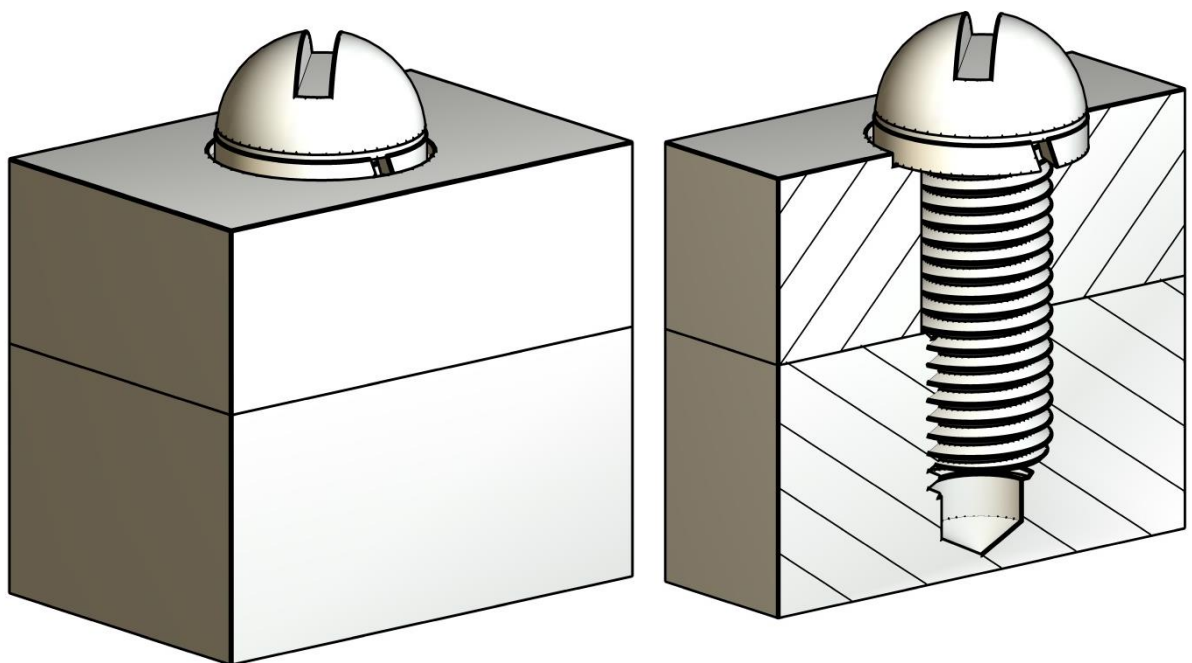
Соединение деталей стандартными крепежными изделиями – винтом с полукруглой головкой (ГОСТ 17473-80) и пружинной шайбой (ГОСТ 6402-70), удерживающей винт от самопроизвольного вывинчивания (справа изображение выполнено условно в разрезе)
